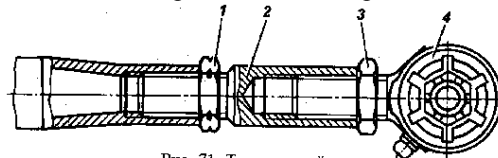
Тяга рулевой трапеции: 1 -гайка с левой резьбой; 2 -регулируемый штуцер; 3 -гайка с правой резьбой; 4 - шарнир
